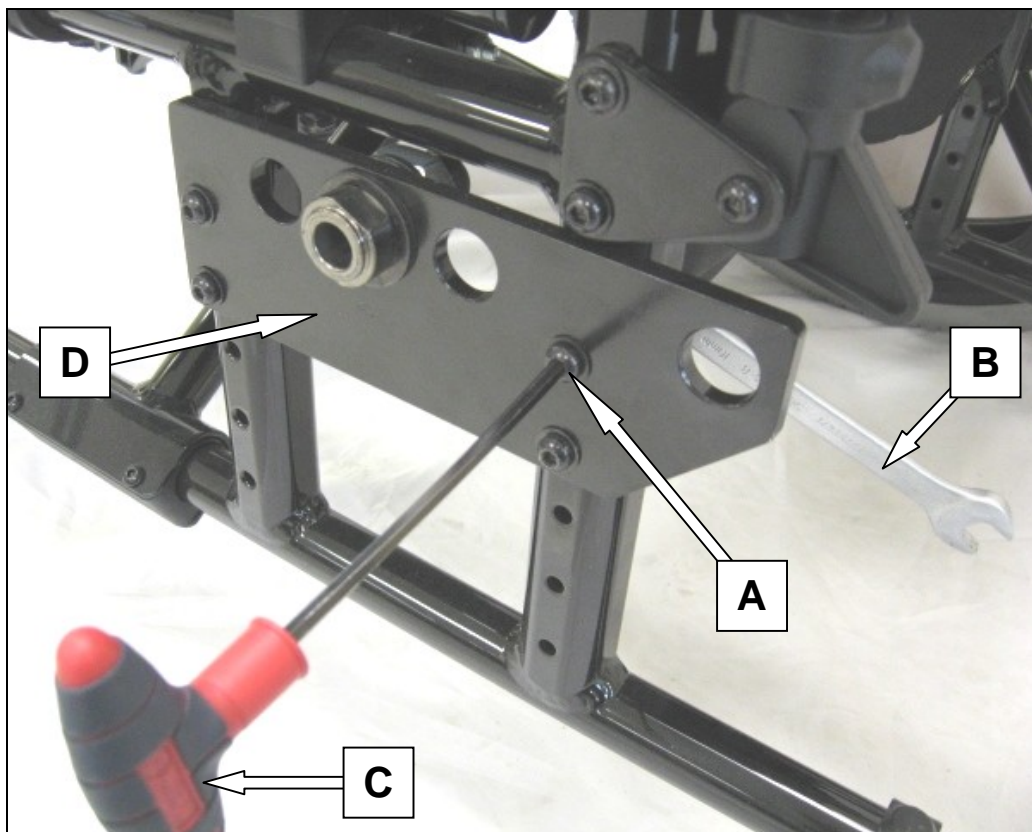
B : Ajustement de la plaque multiposition en hauteur.
